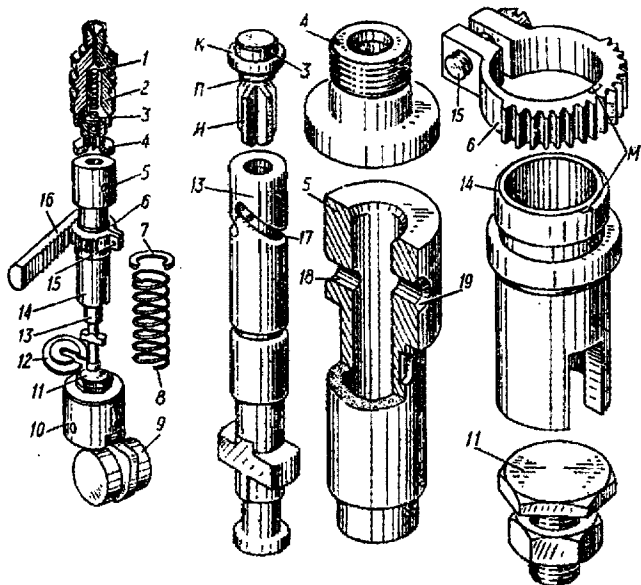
Детали секции УТН-5: 1 – пружина клапана; 2 – штуцер; 3 – нагнетательный канал; 4 – седло клапана; 5 – гильза плунжера; 6 – зубчатый венец; 7 и 12 – опорные тарелки плунжера; 8 – пружина; 9 – кулачковый вал; 10 – толкатель; 11 – регулировочный винт; 13 – плунжер; 14 – поворотная втулка; 15 – стяжной винт; 16 – рейка; 17 – разгрузочный паз; 18 – перепускное отверстие; 19 – впускное отверстие; Н – направляющая часть клапана; К – запорный конус; П – разгрузочный пояс; М – установочные метки
